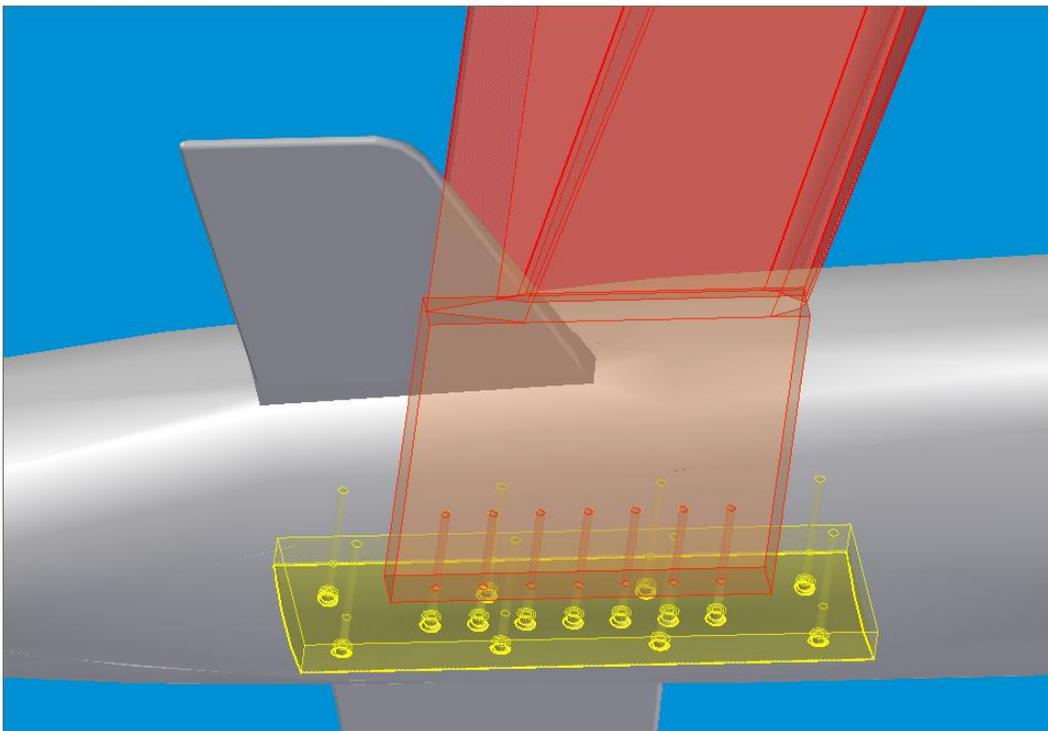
Ensamblaje de la quilla con el bulbo.
